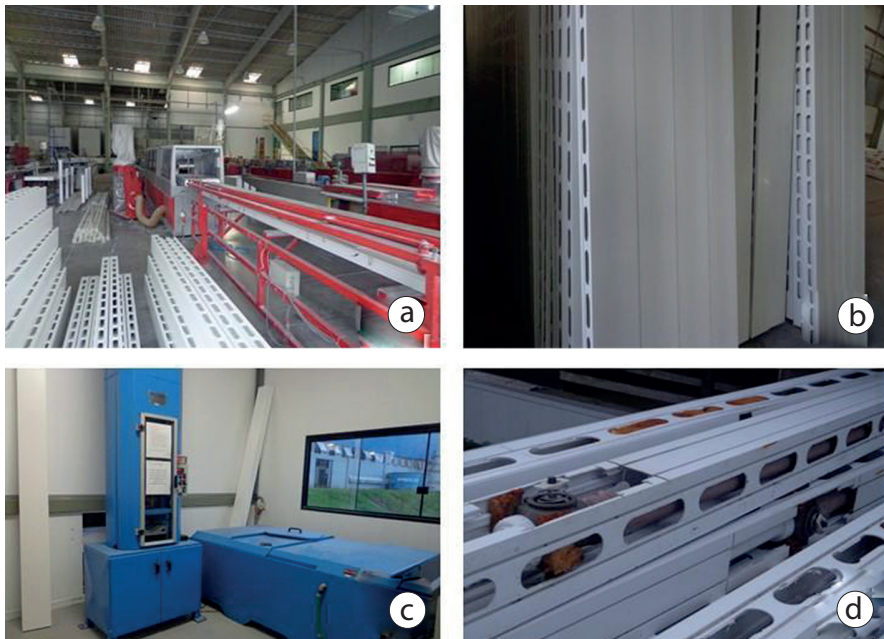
Industrialização dos painéis de PVC. (a) Máquinas para produção e corte dos perfis de PVC; (b) Painéis montados e modulados de PVC; (c) Sala de ensaios; (d) Kit hidráulico embutido no perfil de PVC. Fonte: Autores (2016).
